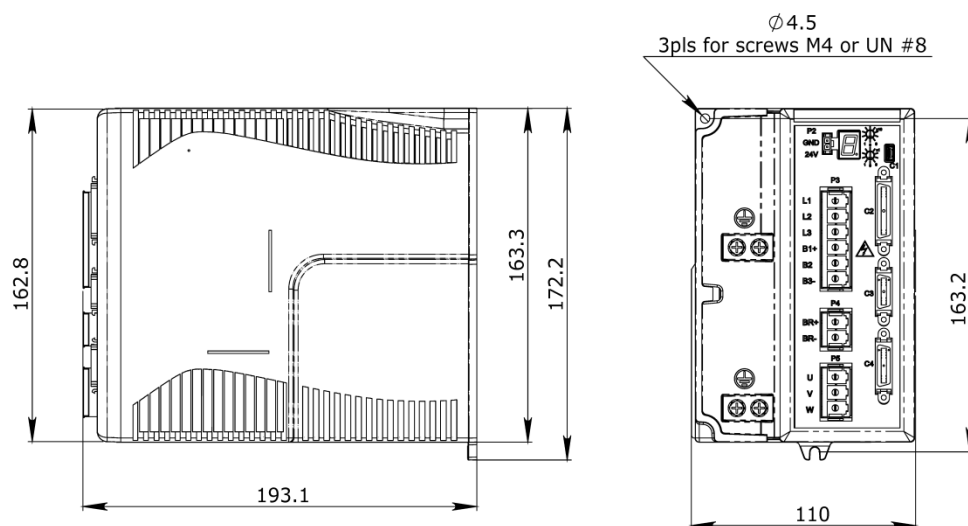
CDHD-003/CDHD-006 (400/480 VAC) – 尺寸 (mm)
